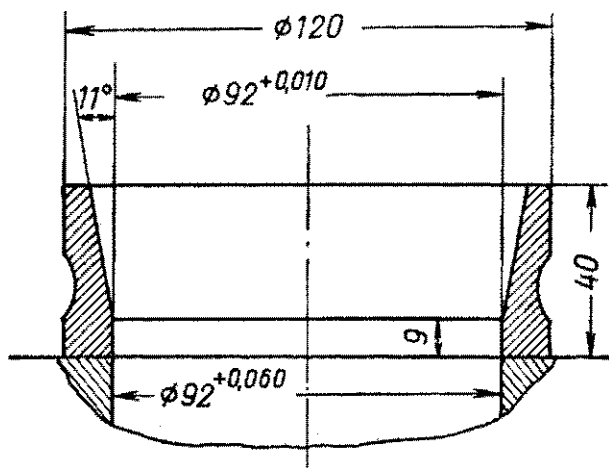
Конусное кольцо для постановки поршня с кольцами в цилиндр
